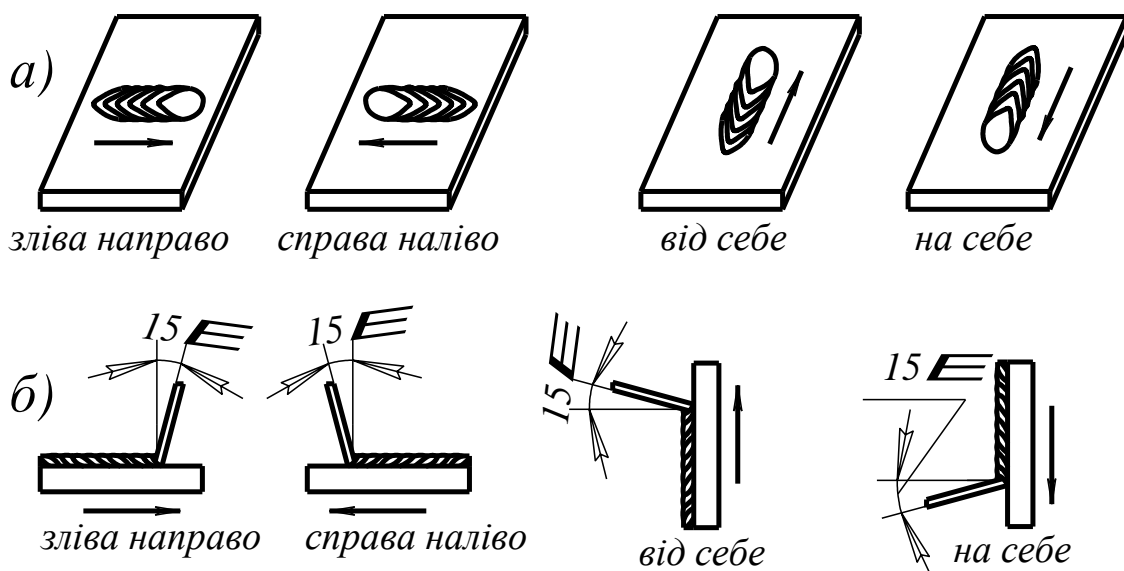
Напрямок зварювання – а) і нахил електрода – б)
